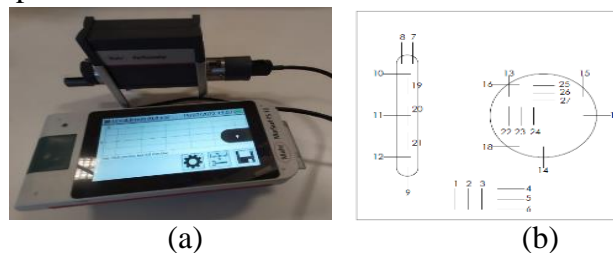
Avaliação da rugosidade superficial dos provetes soldados: (a) MarSurf PS10; (b) Zonas de medição de rugosidade num provete soldado.
